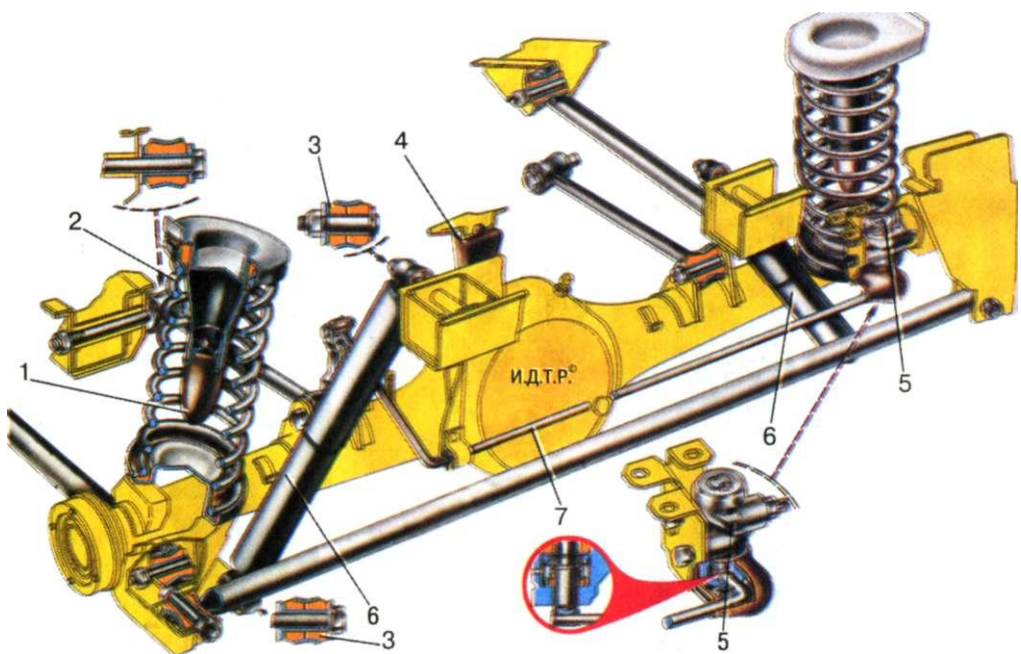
Задняя подвеска с пружинными рессорами: 1 - буфер хода сжатия; 2 - пружина подвески; 3 - резиновые втулки проушин амортизатора; 4 - дополнительный буфер сжатия; 5 - регулятор давления задних тормозов; 6 - амортизаторы; 7 - рычаг привода регулятора давления
